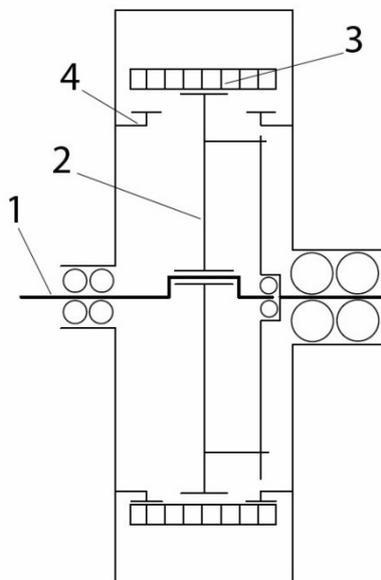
Схема планетарного редуктора с зубчато-цепной гибкой связью
